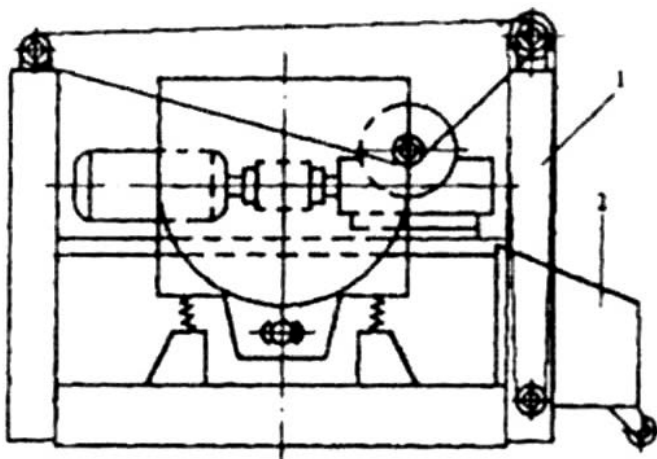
Схема устройства для механизации загрузки и разгрузки вибрационного станка УВГ-100: 1 - привод; 2 - сборник деталей
